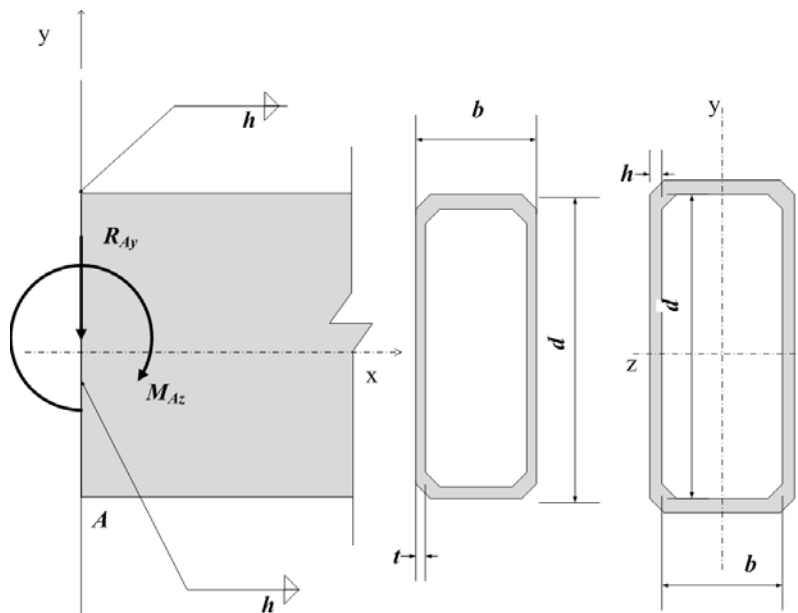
Reacciones y esquema de soldadura en extremo A de Viga 3 (plano xy).
